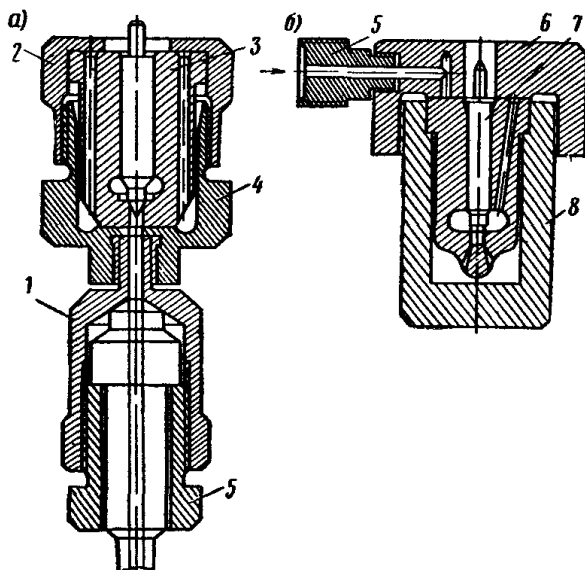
Пристосування для випресовки пригорілих голок форсунок
